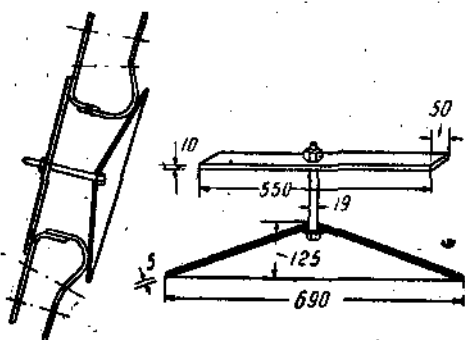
Предохранительный экран для сварки лавов.
